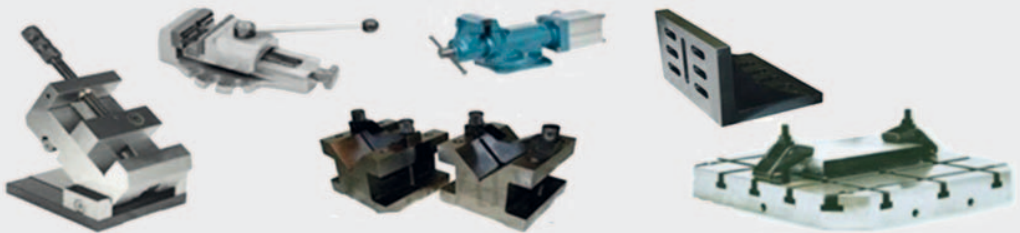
Різновиди пристосувань для установки деталей при свердлінні
